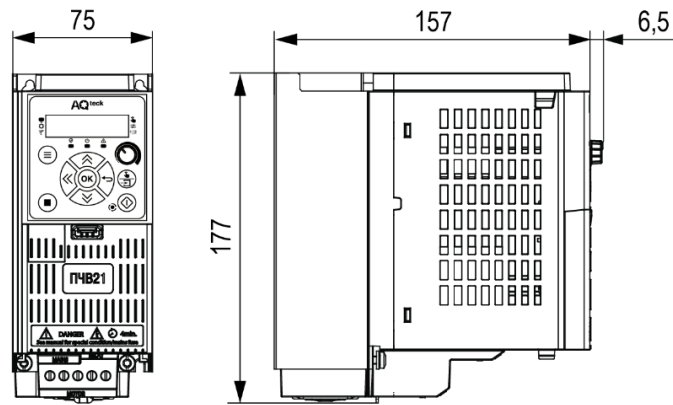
Габаритні розміри ПЧВ у корпусі 2
